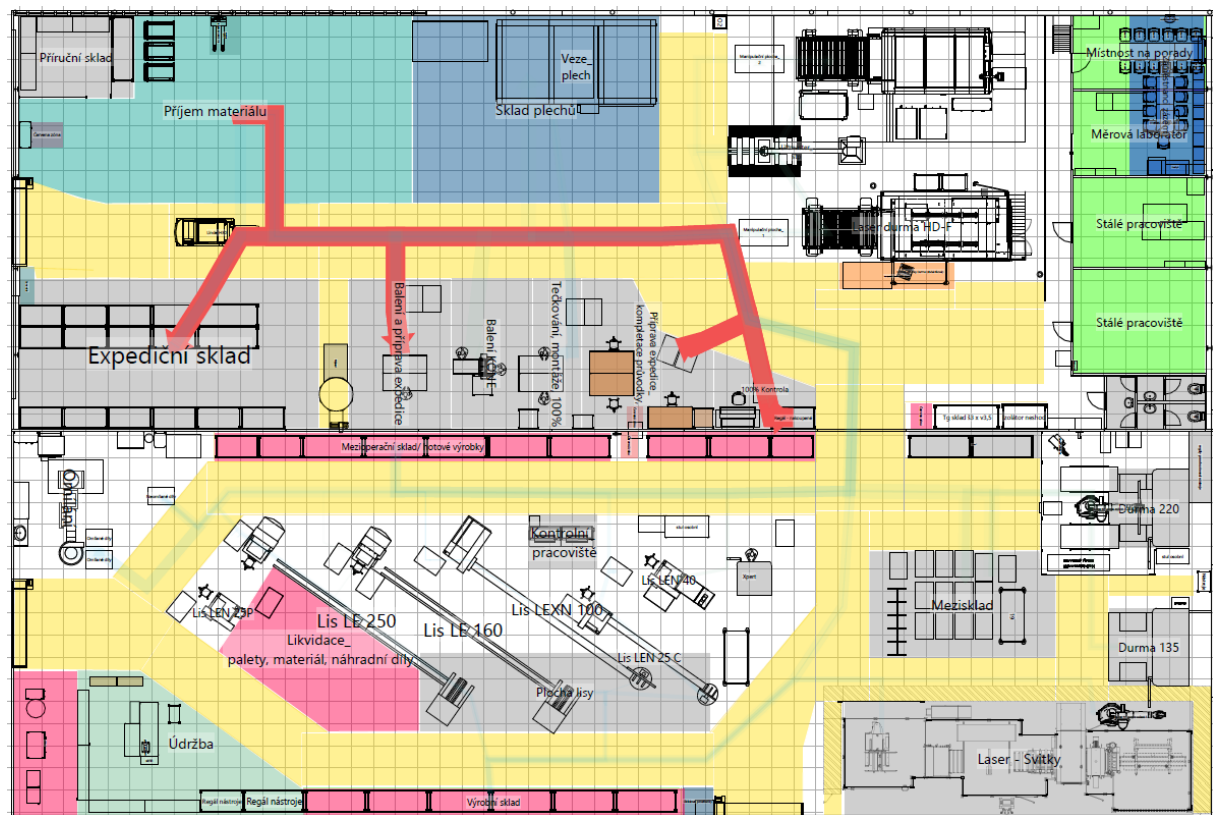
Sklad plechových tabulí – Varianta 3
